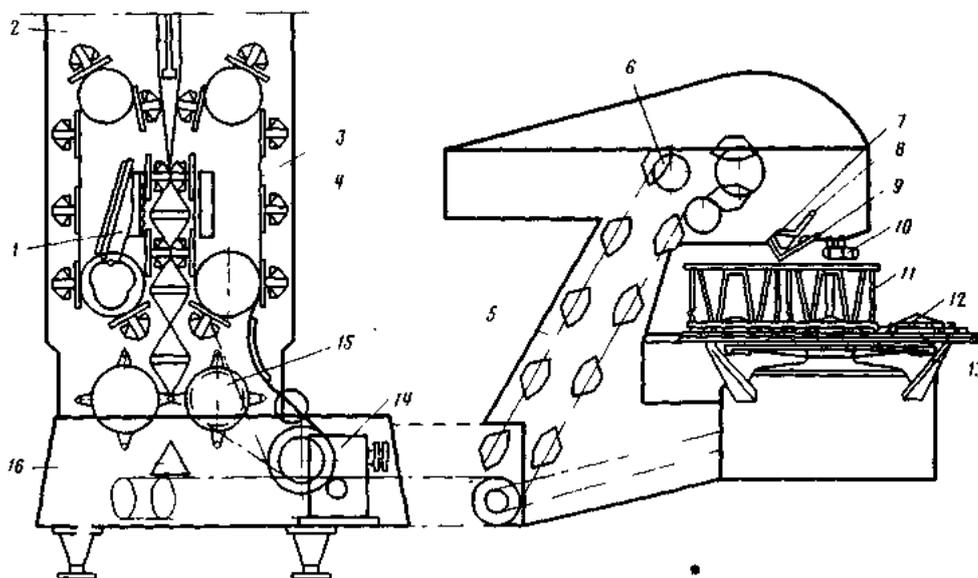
Механизм образования и укладки пакетов в корзины: 1 - клин механизма прижима; 2 - бумажный рукав; 3 - вертикальный цепной транспортер; 4 - зажим; 5 - конвейер; 6 -ковш; 7 - желоб; 8 - толкатель; 9 - заслонка; 10 - разделительная звездочка; 11 - корзина; 12 - поворотный диск для корзин; 13 - поворотный стол укладчика; 14 - червячный редуктор; 15 - крестовина механизма отрезки пакетов; 16 - ловитель для отрезанных пакетов
